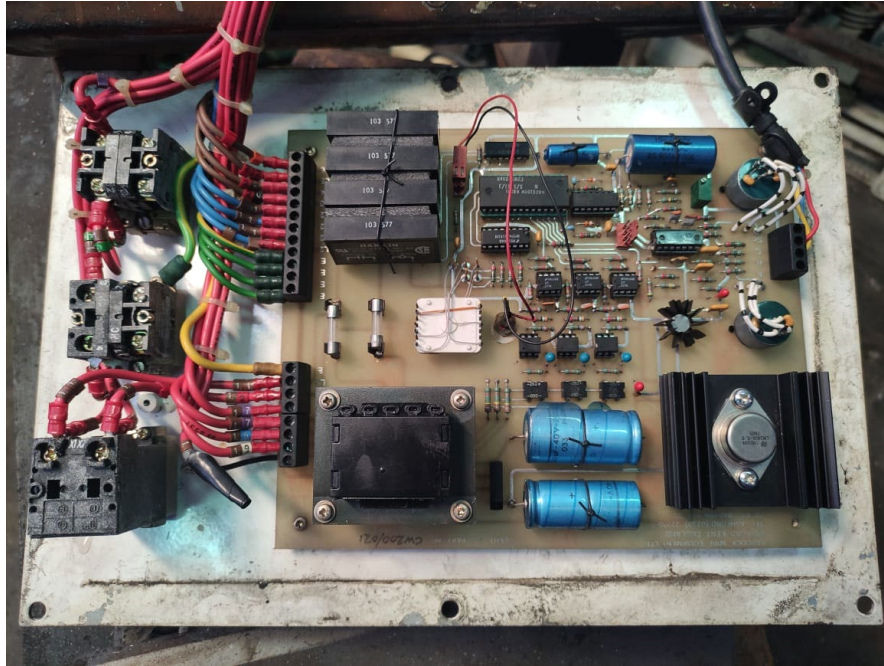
Tarjeta electrónica de control de la Soldadora en Frio.
